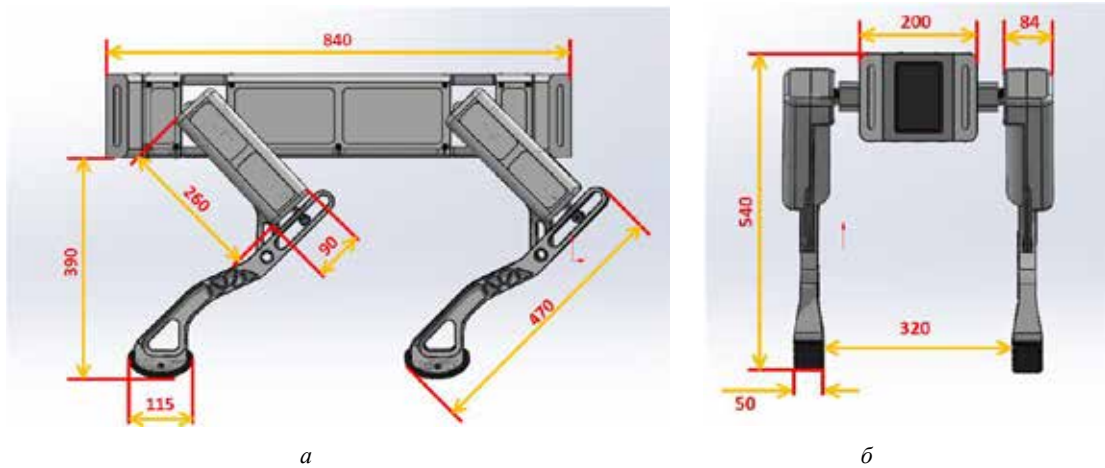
Модель прототипу конструкції: а – вид збоку, б – вид спереду
